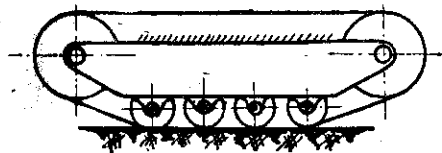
Направляющее колесо при гребневом зацеплении с натяжным приспособлением.
